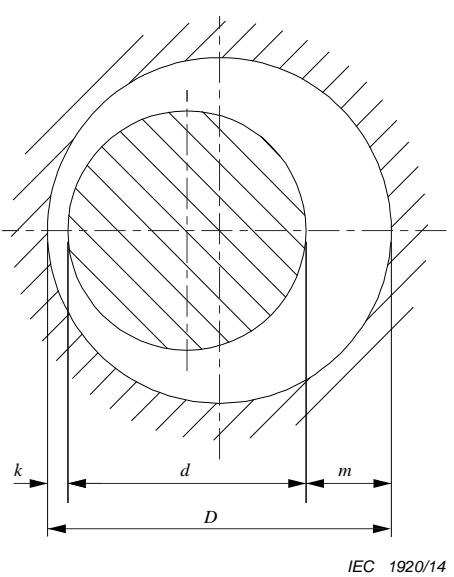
Exemple de joint à labyrinthe pour arbre de machine électrique tournante
